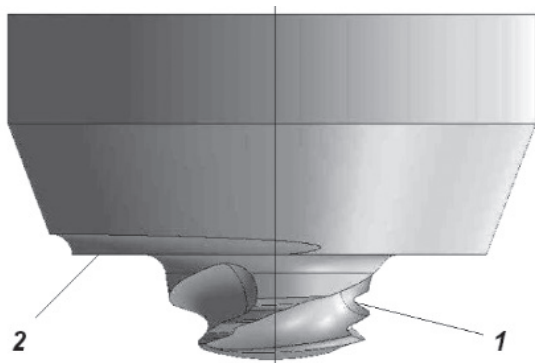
Форма инструмента для сварки трением с перемешиванием:
